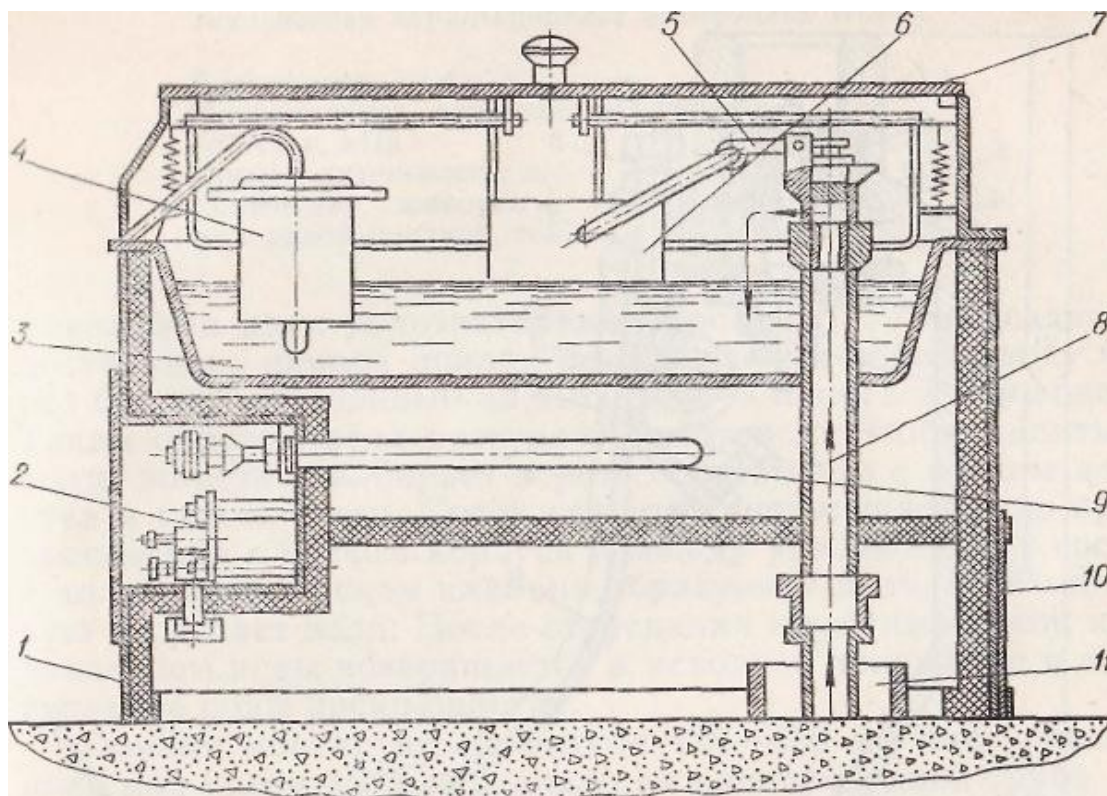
Автопоїлка групова АГК-4А: 1 - корпус; 2 - температурне реле; 3 - корито; 4 - терморегулятор води; 5 - клапанний
